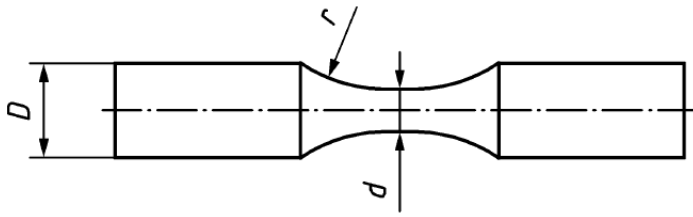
Schematische Zeichnung einer Umlaufbiegeprobe [28]
